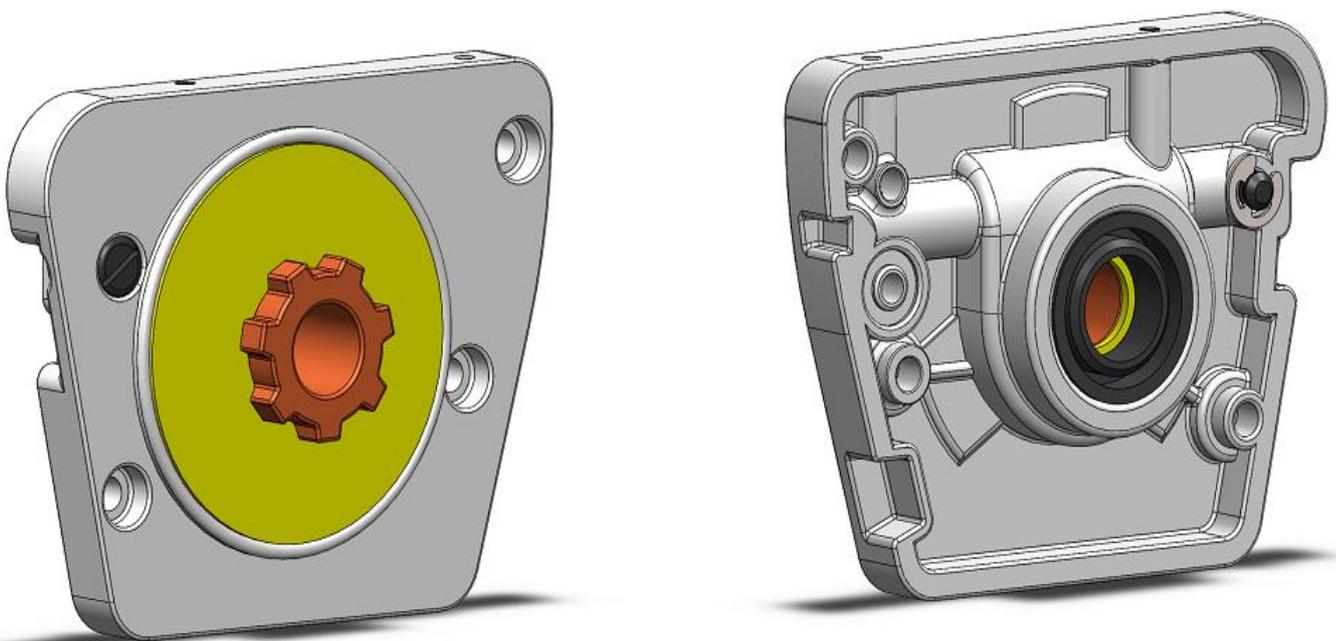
Pompe à huile automatique dans ses deux vues avant et arrière
